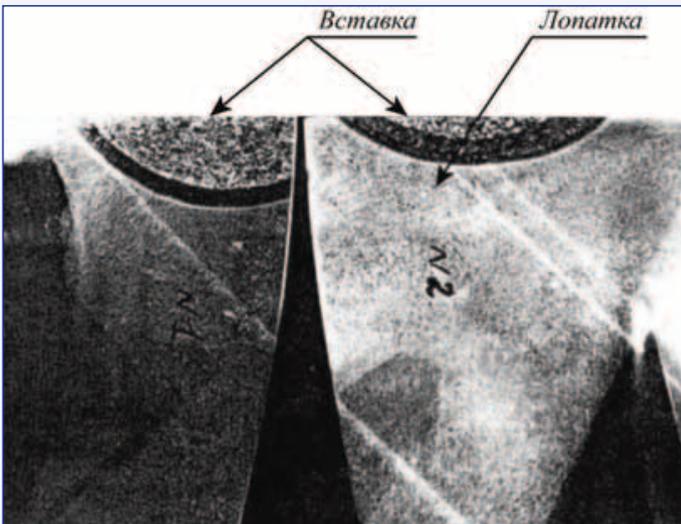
Макроструктура металла лопаток после электронно-лучевой сварки вставок и механической обработки
